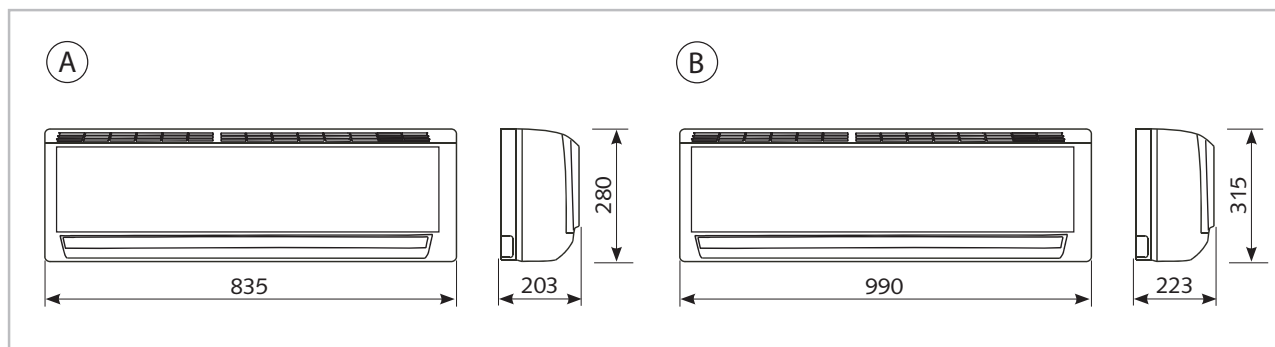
Geräteabmessungen (Alle Angaben in mm)
